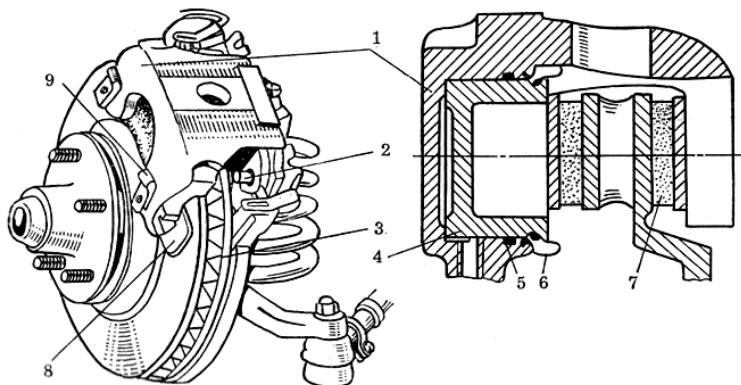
Дисковый тормозной механизм с плавающей скобой и вентилируемым диском: 1 — подвижная скоба с колесным цилиндром; 2 — направляющий штифт; 3 — диск; 4 — поршень; 5 — уплотнительное кольцо; 6 — пылезащитный чехол; 8 — колодки; 7 — накладки; 9 — антивибрационные пластинчатые пружины
